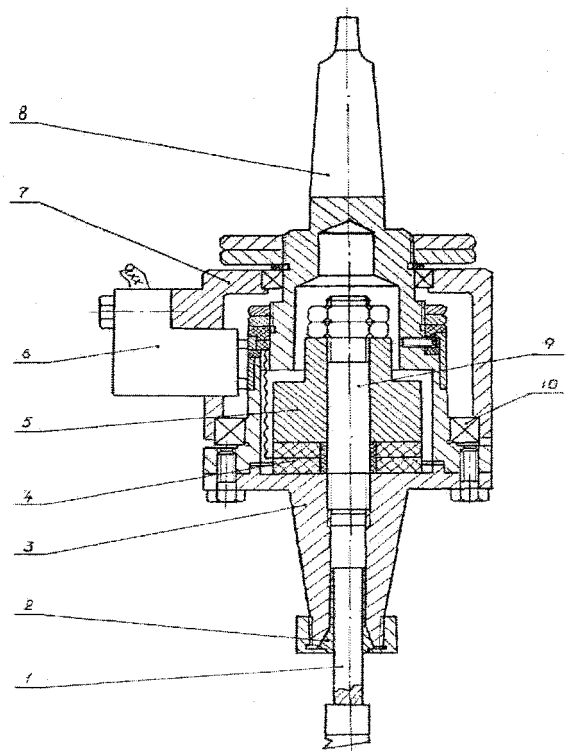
Ультразвуковое устройство для нарезания резьбы резцом
